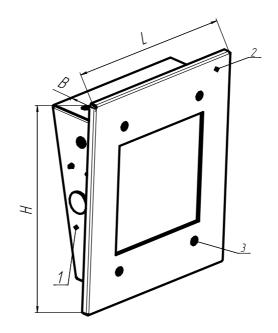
Общий вид светильника ДБО76 DS 1- Корпус в сборе; 2 - Рассеиватель в металлической рамке; 3 - Винты
